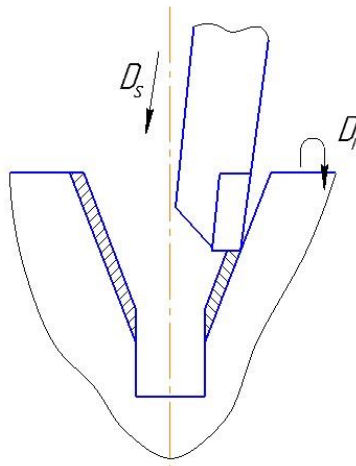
Обработка боковых поверхностей ручьев проходным резцом
